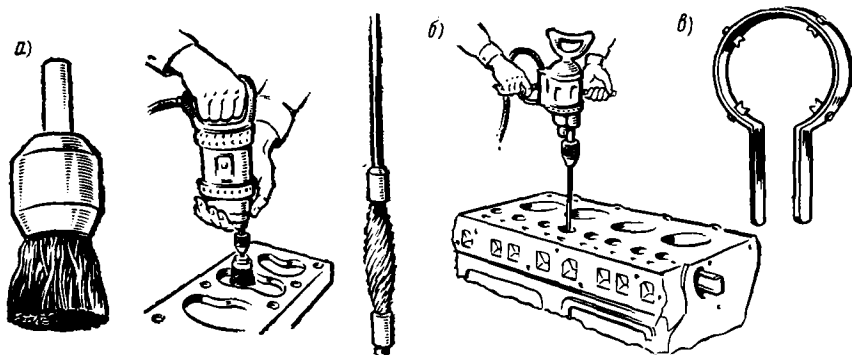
Приспособления для очистки от нагара и других отложений: головки цилиндров: б — направляющих втулок клапанов: в — канавок поршней
